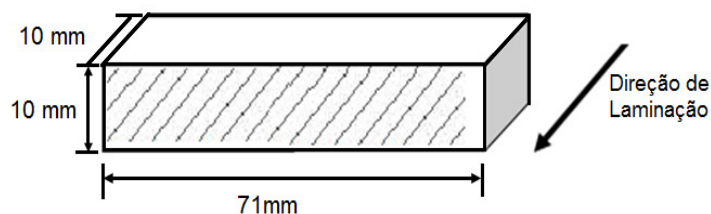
Dimensões de corpos de prova para a simulação de soldagem.
